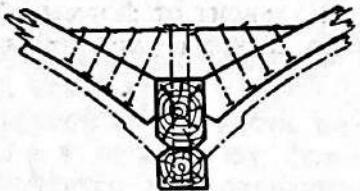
Деревянный флор, установленный поверх шпангоута.
